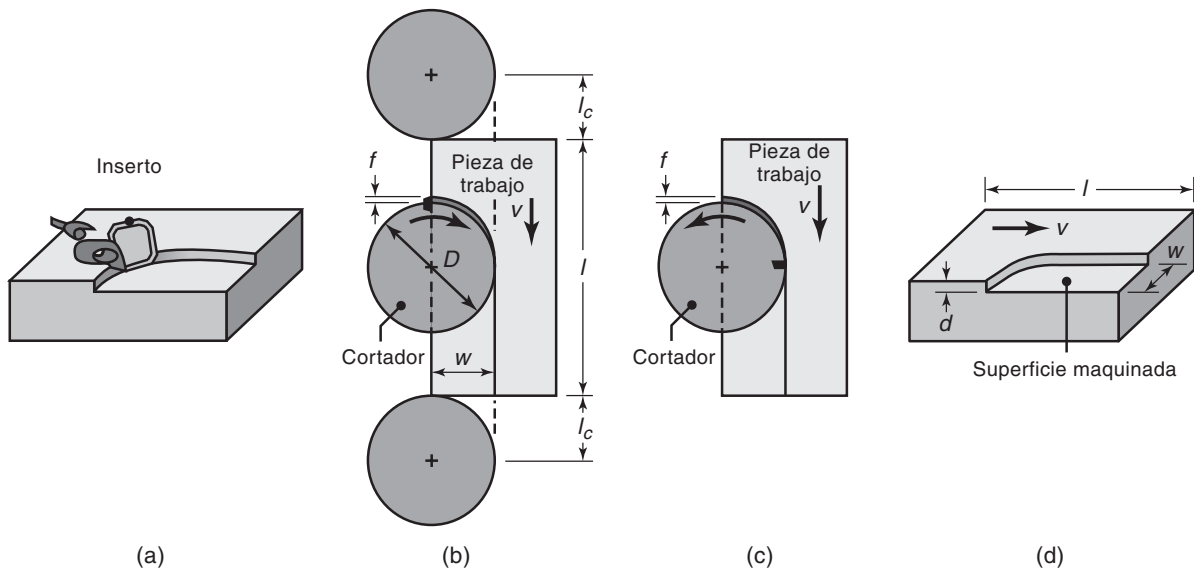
Operación de fresado de careado que muestra (a) la acción de un inserto en el fresado de careado; (b) fresado concurrente; (c) fresado convencional; (d) dimensiones en el fresado de careado. La anchura de corte, w , no es necesariamente la misma que el radio del cortador.
